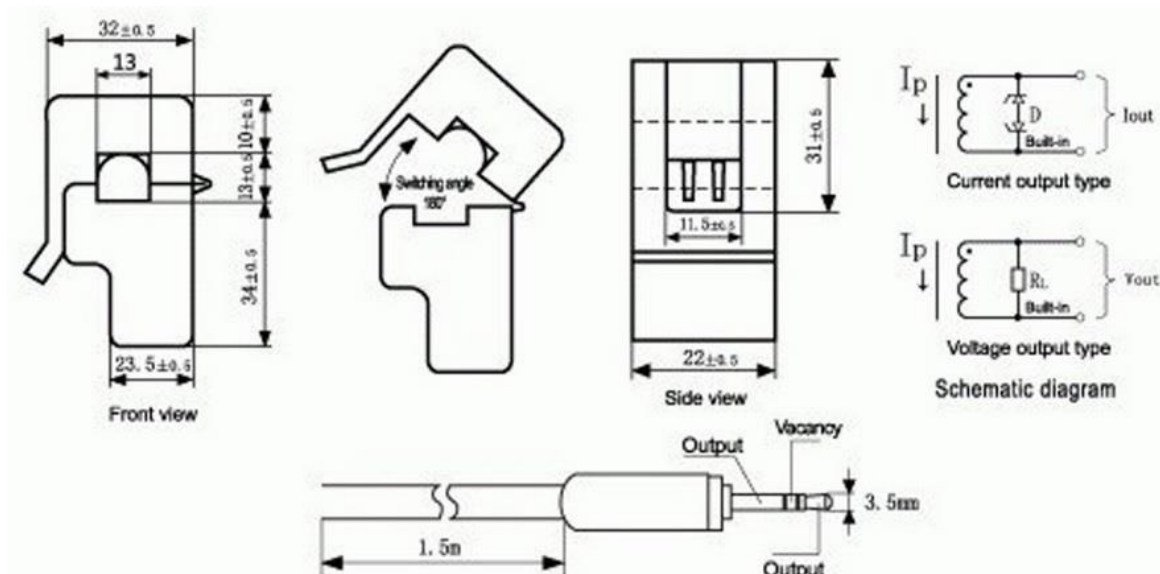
Dimensões do sensor de efeito Hall SCT013-100A.
